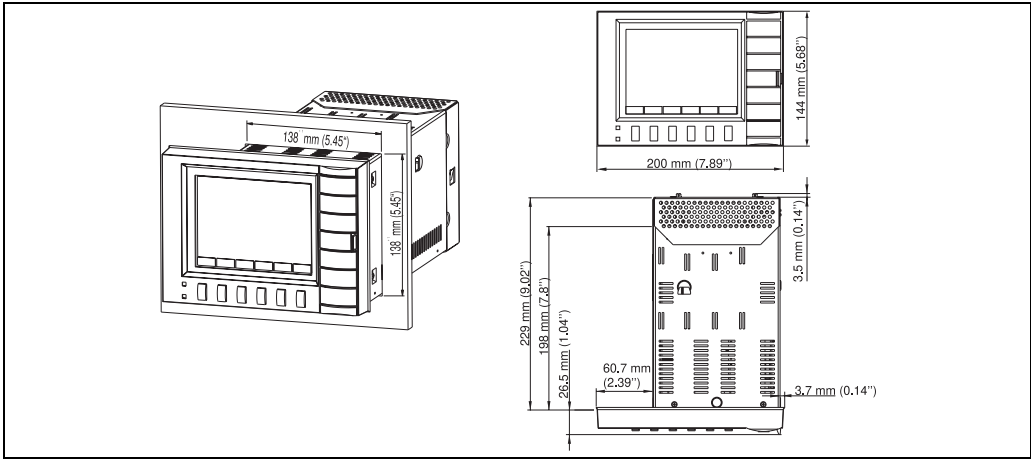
dimensiones para el montaje en panel de la versión con frente de fundición inyectada
